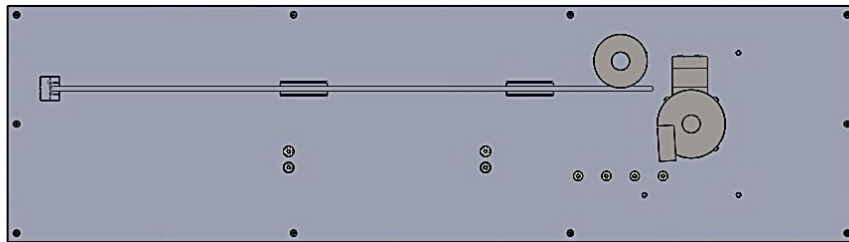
Modelo CAD del ensamble de las piezas de la máquina.
